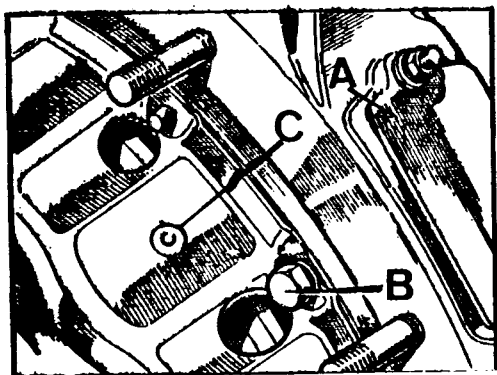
Desmontaje del plato de presión y disco de embrague
